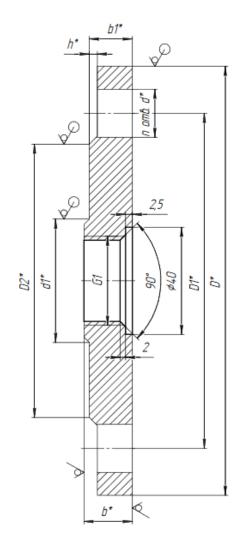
Монтажная часть ЭЛЕМЕР-УПП-11 с различными типами поплавков.
